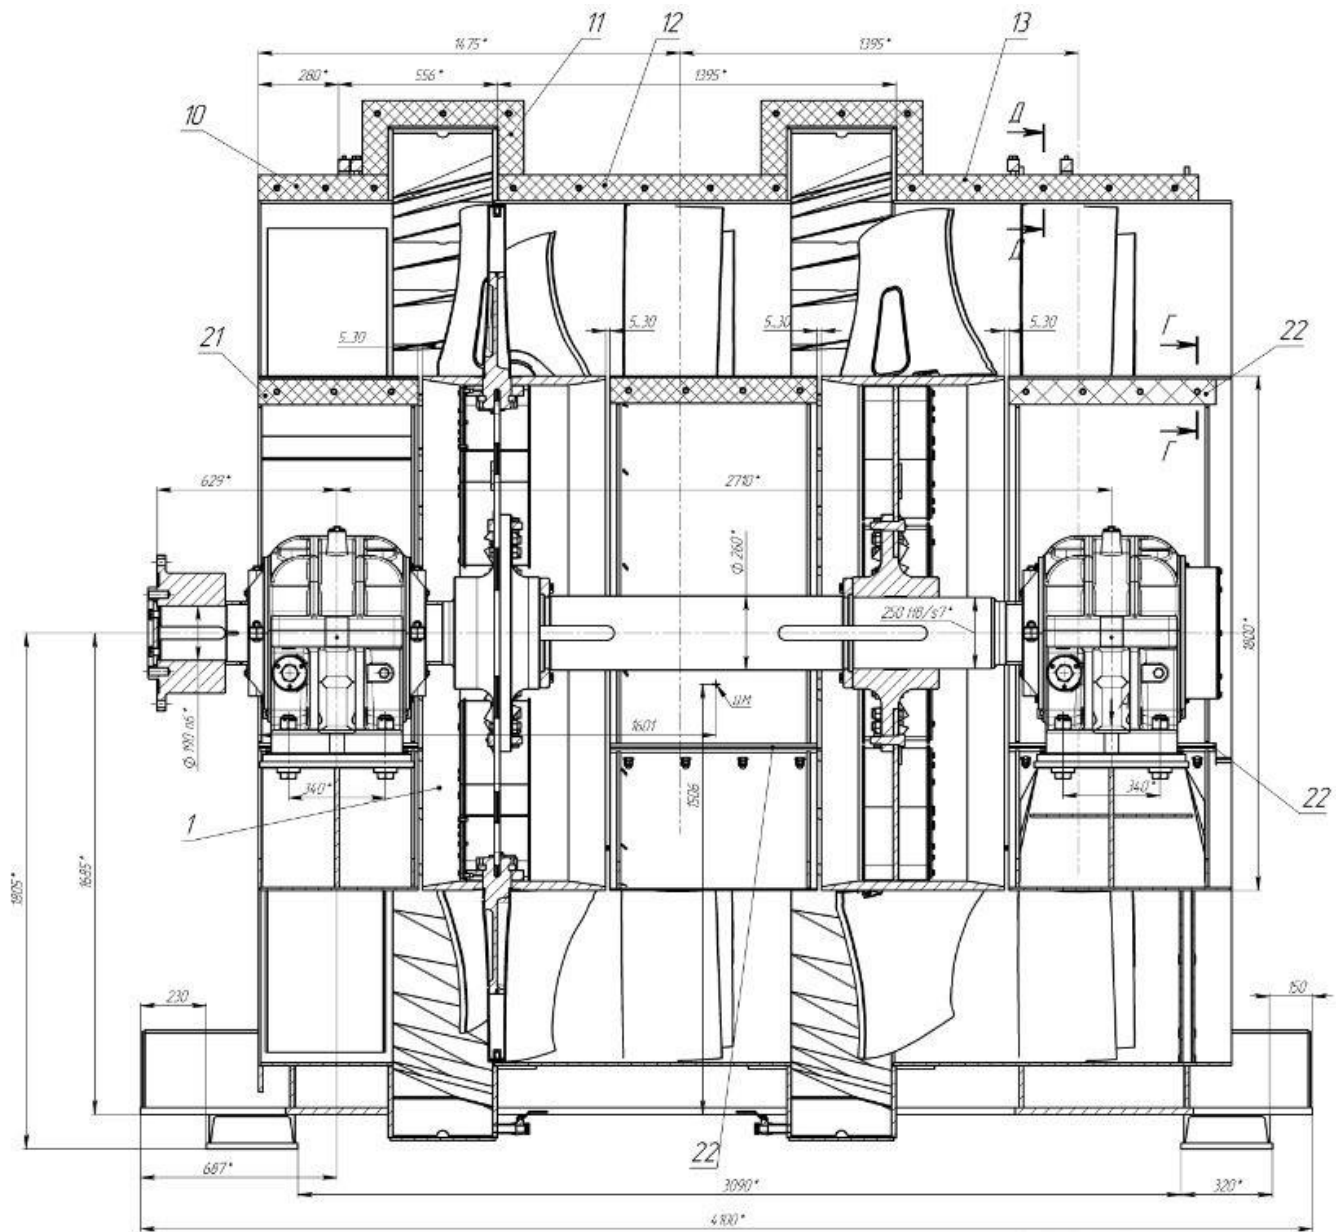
Корпус з противозривним пристроєм та ротором.
